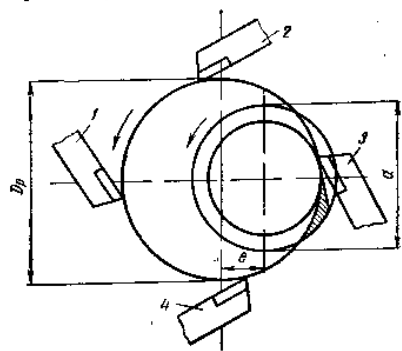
Схема вихревого фрезерования тангенциально расположенными резцами:
